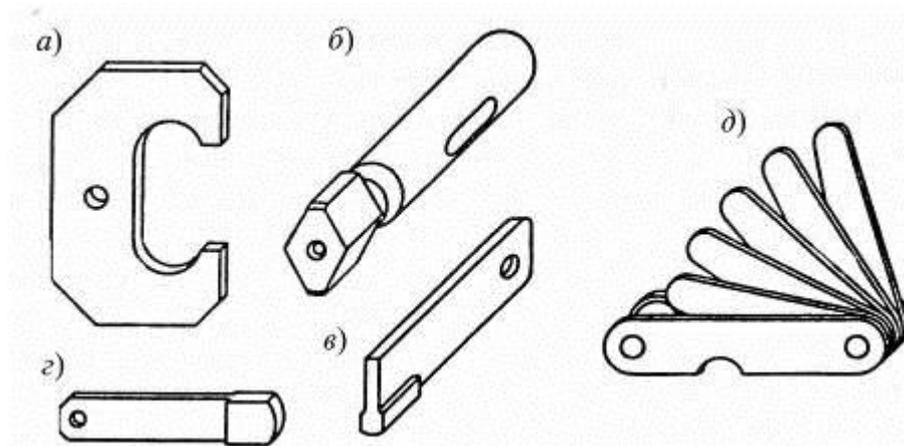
Дефектовочные калибры: а — скоба; б — пробка; в — калибр для проверки ширины паза шлицевой втулки; г — калибр для проверки ширины сегментного шпоночного паза; д — набор калибров для проверки ширины поршневых канавок
